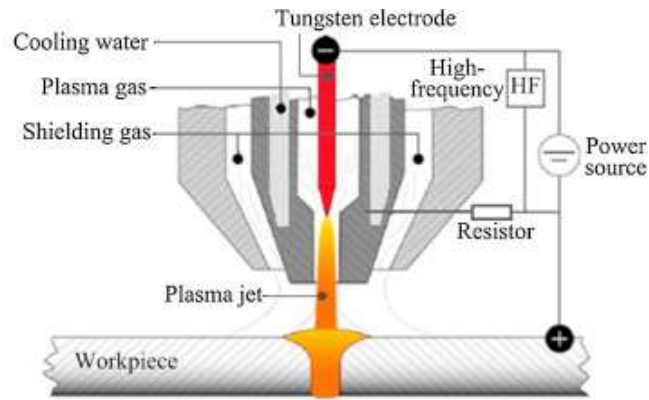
4 Le procédé de soudage plasma [24]
